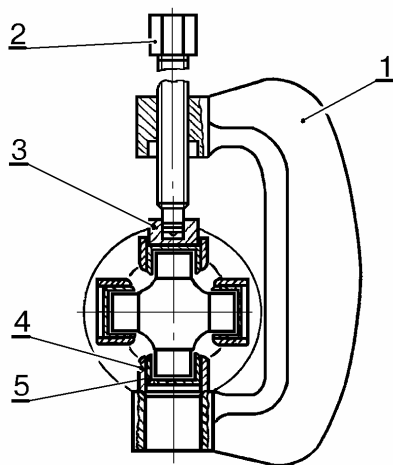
Выпрессовка подшипников крестовины 2101-2202025-01:
